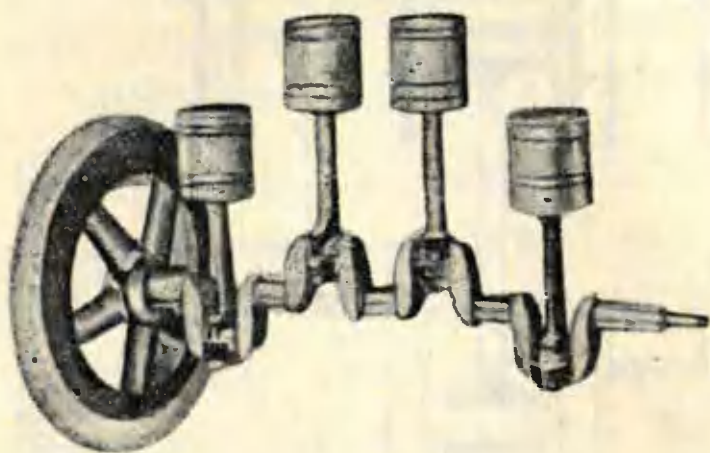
Вот как выглядели поршни с коленчатым валом и с маховым колесом, когда их вынули из цилиндров двигателя.
